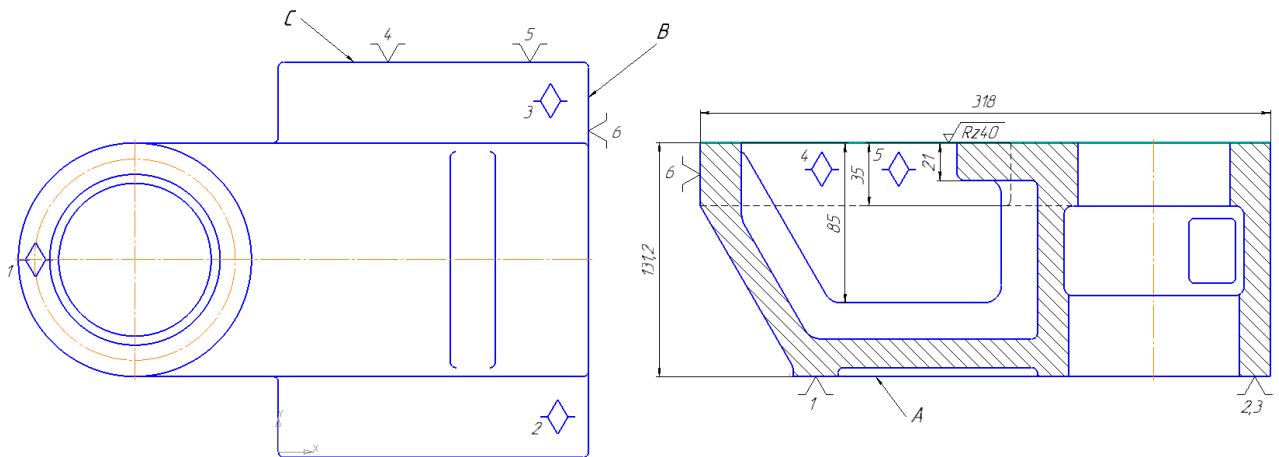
Схема базування та закріплення заготовки на операції 020 фрезерна
